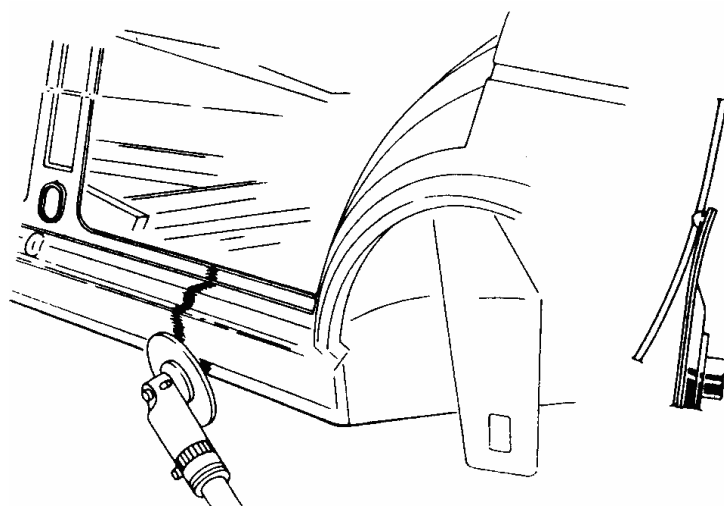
Esmerilado del cordón de soldadura.
